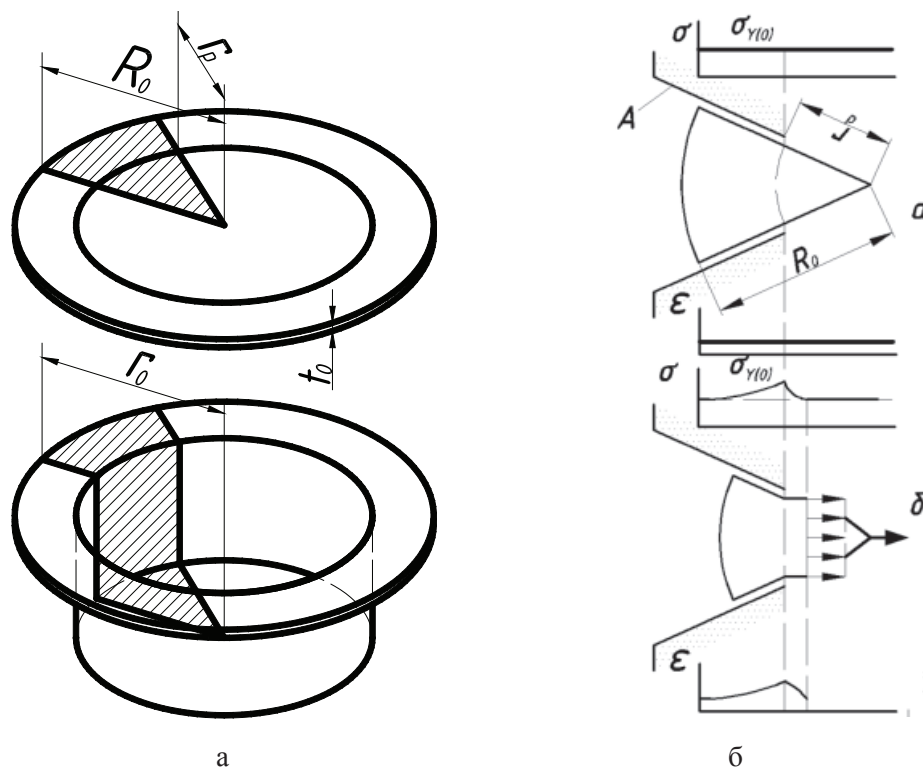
Нестационарная вытяжка листового металла: а – схема операции; б – схема свертки сектора заготовки
